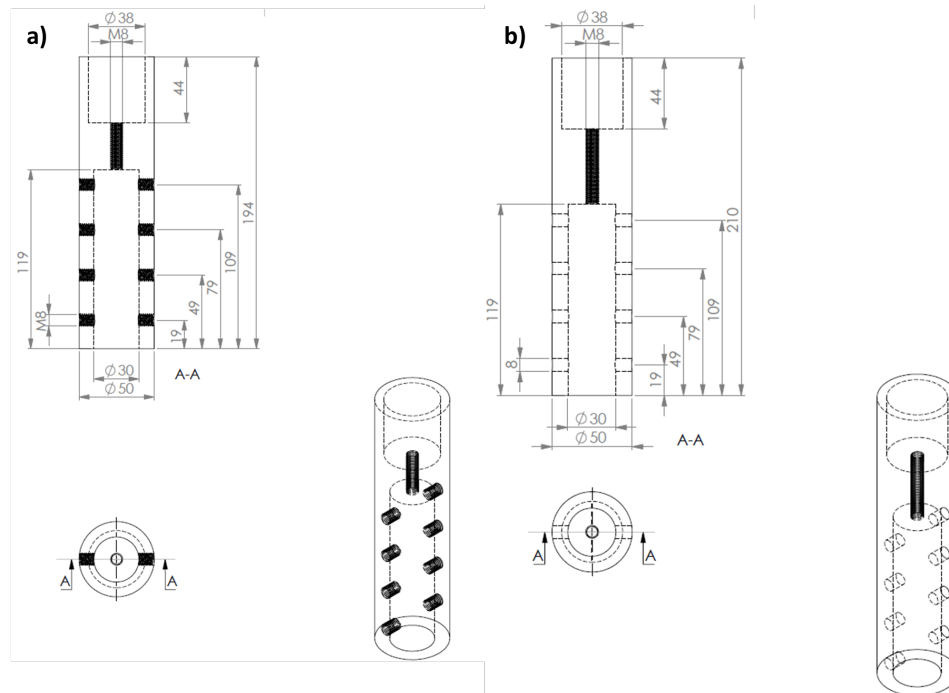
Konstruktionszeichnung der SPQR-Aufsätze für das MARES mit: a) 194 mm langer Aufsatz mit M8 Gewindebohrungen und b) 210 mm langer Aufsatz mit 8mm Bohrungen ohne Gewinde. Quelle: Eigene Abbildung.
